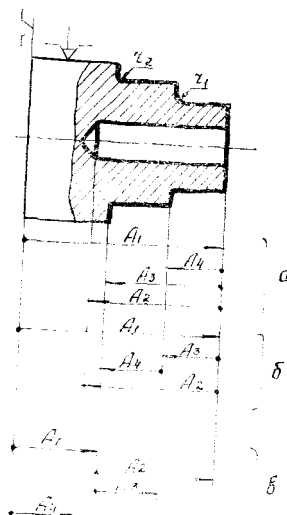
Оптимальные варианты простановки размеров: а — товарно-револьверный станок; б — токарный с ЧПУ; в — многорезцовый.
